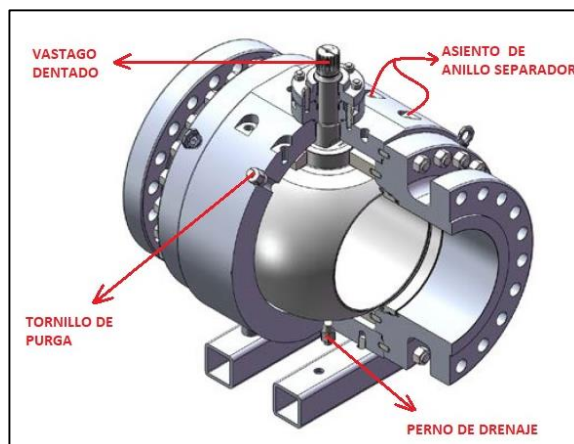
Vista isométrica de la válvula de bloqueo automático.
